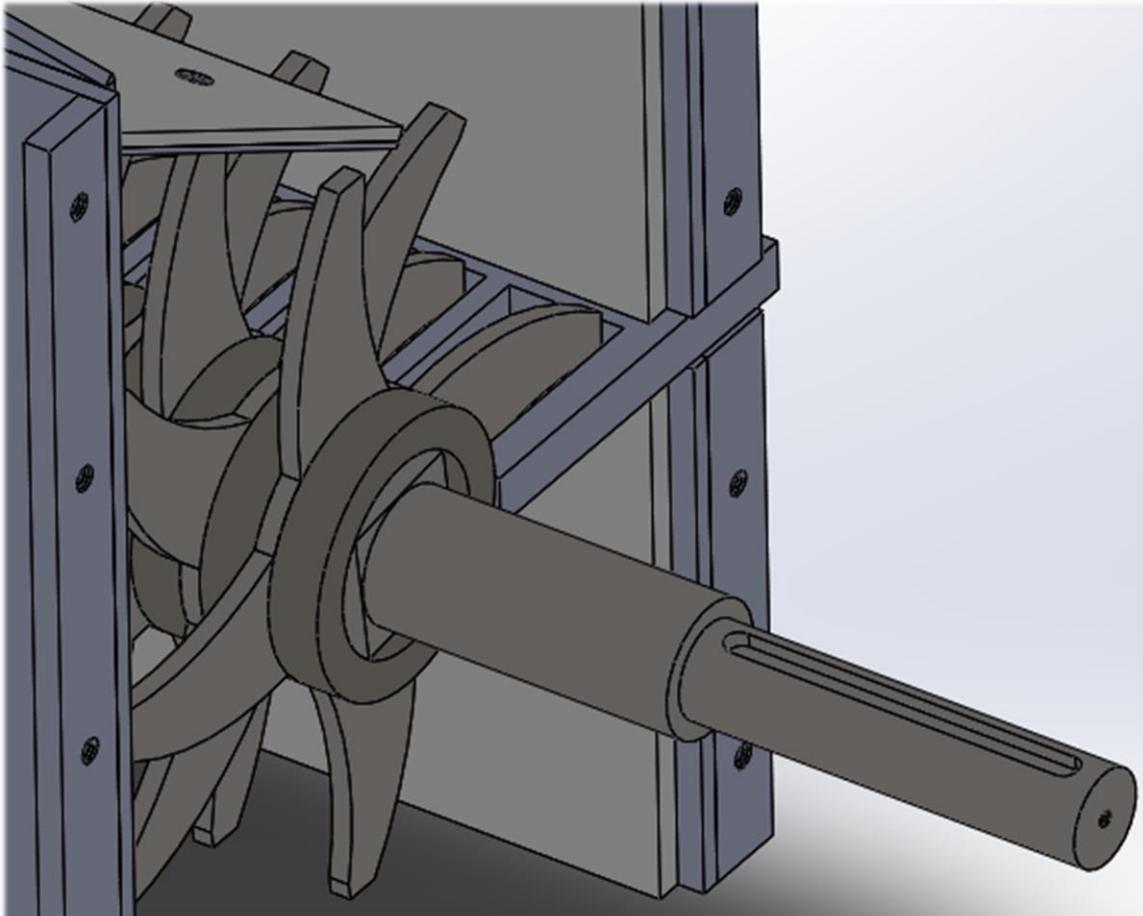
Detalle del montaje del eje con estrellas de la caja de triturar.
